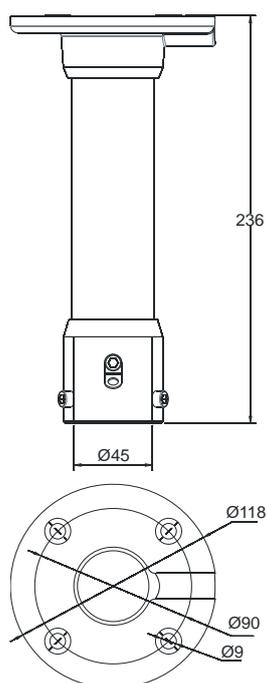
Bild mit den Abmessungen der an der Decke montierten Installationshalterung
